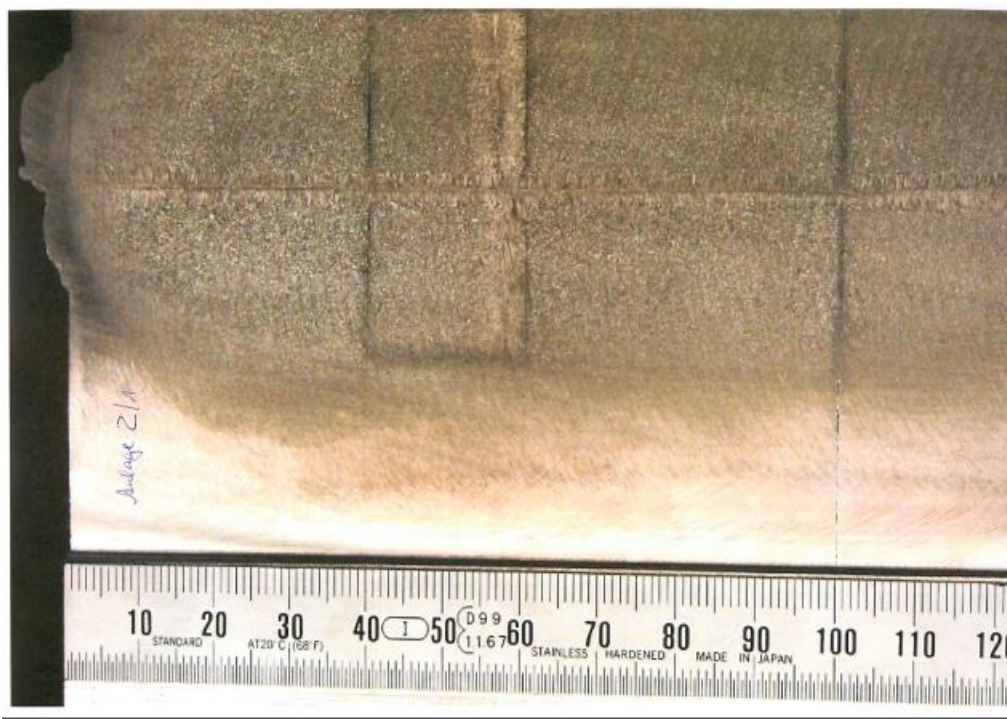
Schliffbild der Überschweißung eines Kühlkanals
